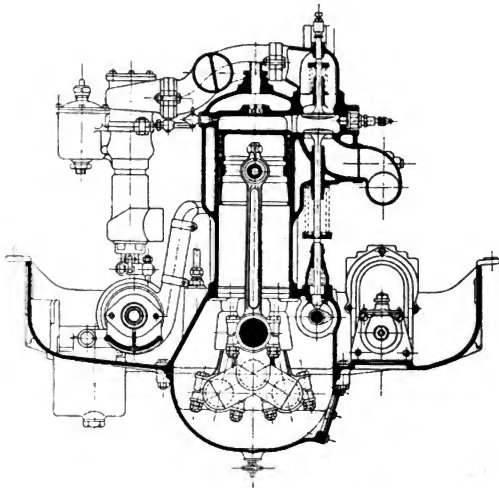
und 385 Vierzylinderiger Horch-Motor.
